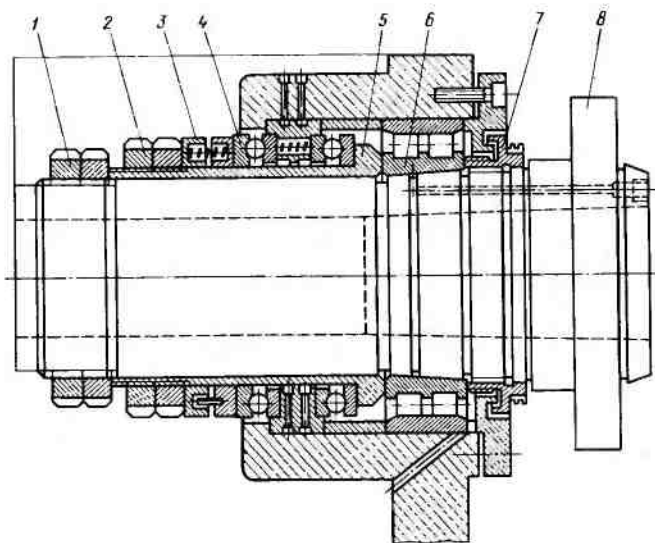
Передняя опора шпинделя токарно-винторезного станка на подшипниках качения:
